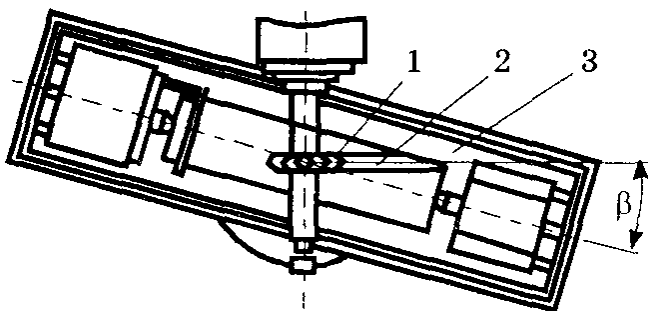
Поворот стола станка при фрезеровании винтовой канавки
